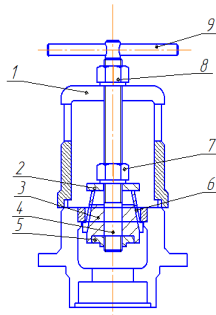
Съемник для выпрессовки обойм с помощью конуса и втулки
